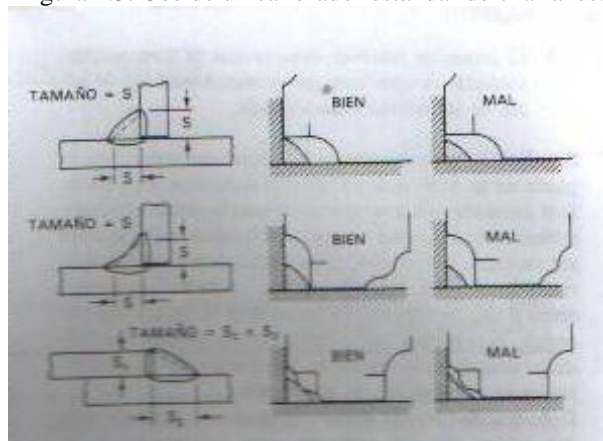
Tamaño de las soldaduras de chaflán y método para determinarlas.
